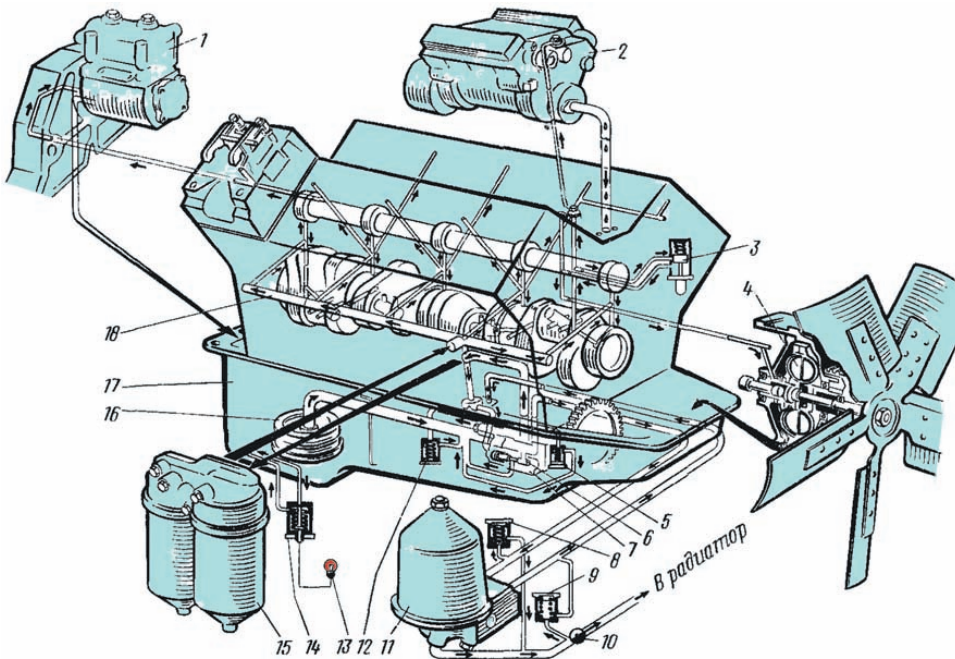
Схема системы смазки: 1 — компрессор; 2 — топливный насос высокого давления; 3 — выключатель гидромфты; 4 — гидромфта; 5, 12 — предохранительные клапаны; 6 — клапан системы смазки; 7 — насос масляный; 8 — перепускной клапан центробежного фильтра; 9 — сливной клапан центробежного фильтра; 10 — кран включения масляного радиатора; 11 — центробежный фильтр; 13 — лампа сигнализатора засоренности фильтра очистки масла; 14 — перепускной клапан полнопоточного фильтра; 15 — полнопоточный фильтр очистки масла; 16 — маслоприемник; 17 — картер; 18 — главная магистраль.
